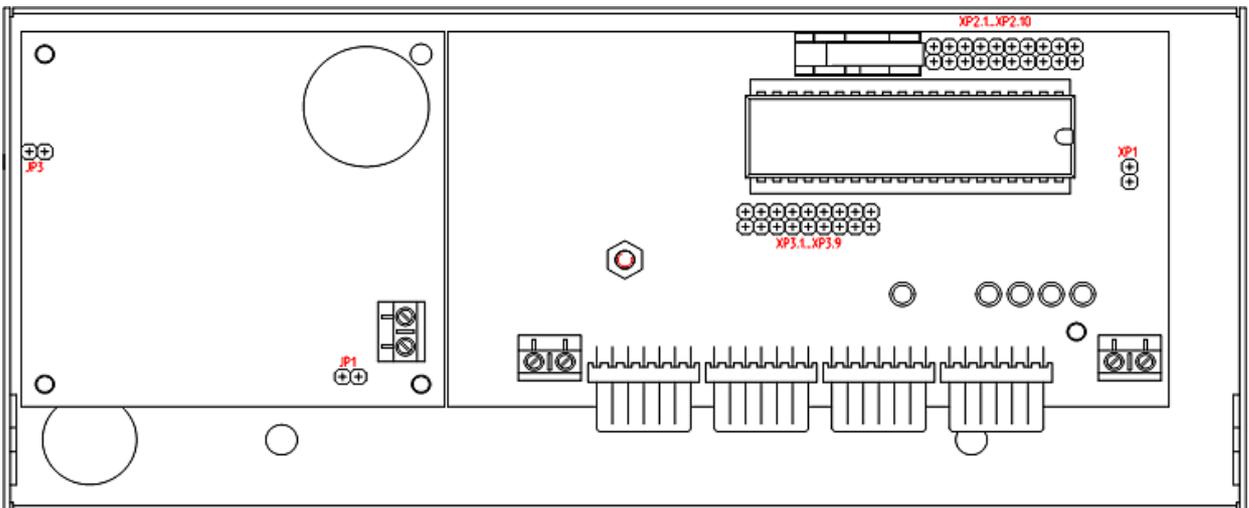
Расположение ИСА-8 и КСП-А4/8 внутри корпуса
